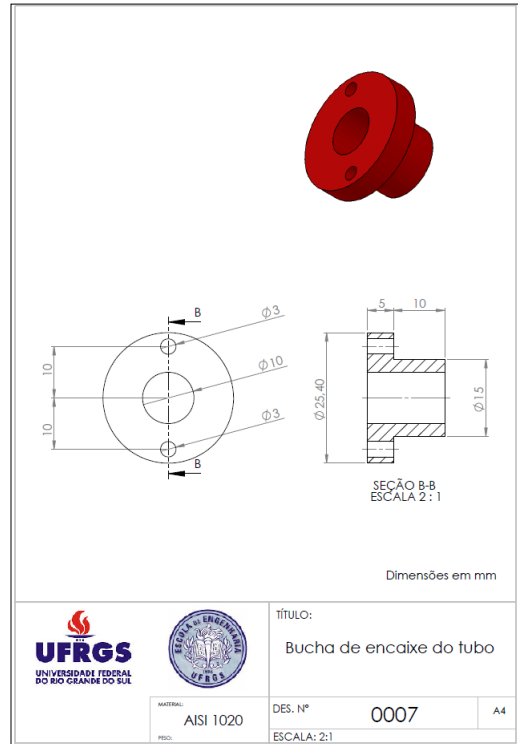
Figura II: Desenho e dimensões da bucha de encaixe do tubo
